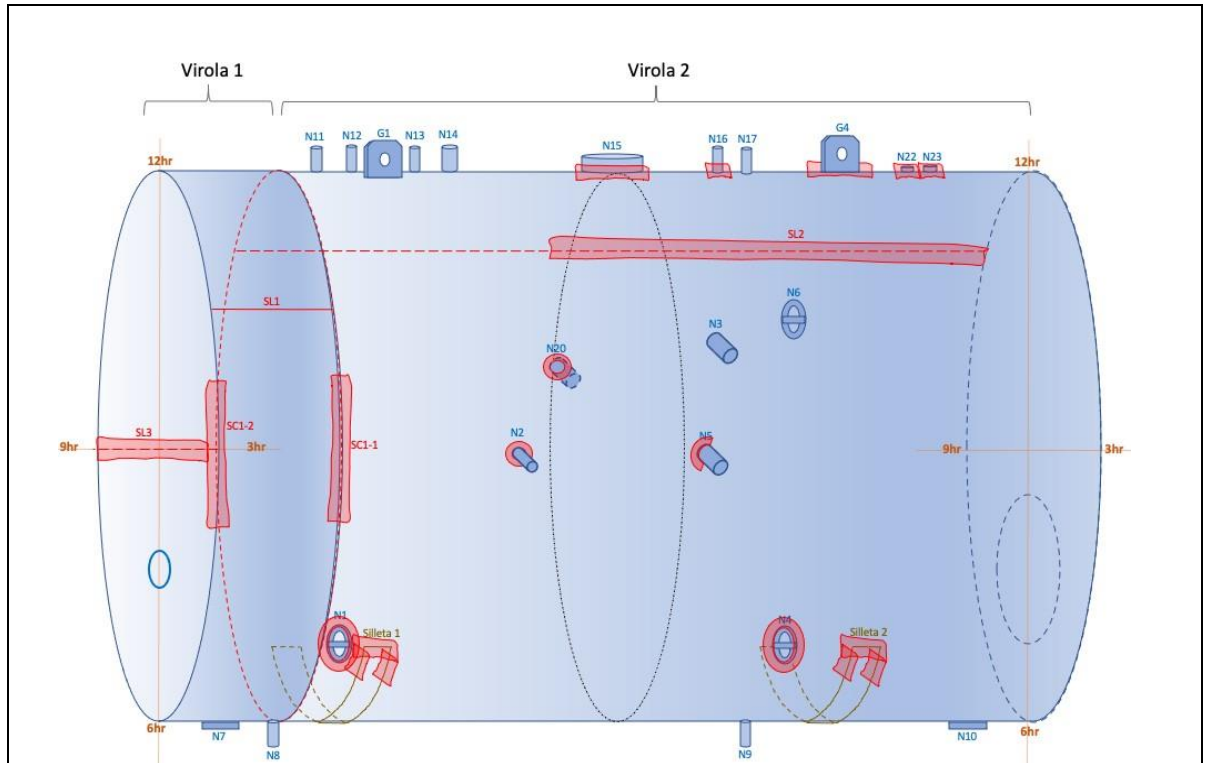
Ubicación sectores inspeccionados por PT en soldaduras a filete de Niples y soldaduras a tope del cuerpo de la caldera de vapor
